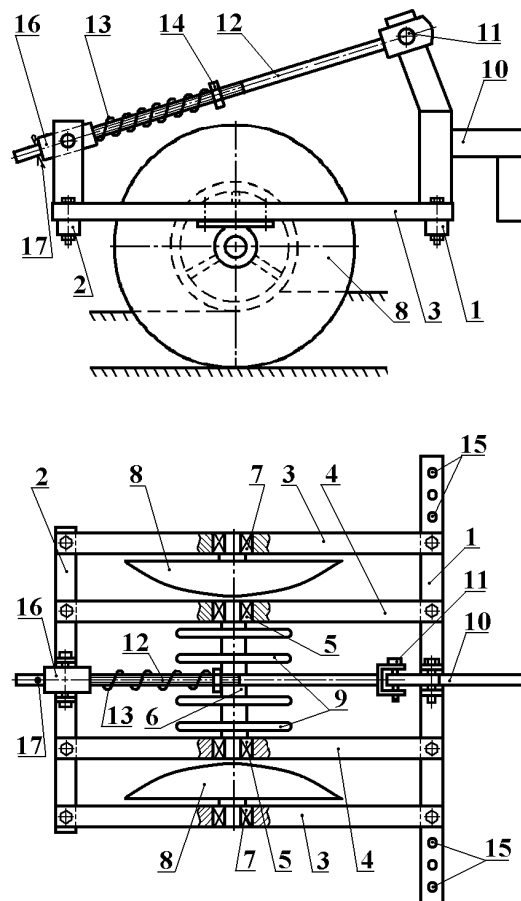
Каток: 1, 2 – балки поперечные; 3, 4 – балки продольные; 5, 7 – подшипники; 6 – ось; 8 – сферические диски; 9 – прикатывающие кольца; 10 – кронштейн; 11 – палец; 12 – штанга; 13 – пружина; 14 – гайка; 15 – отверстие; 16 – муфта; 17 – шплинт
